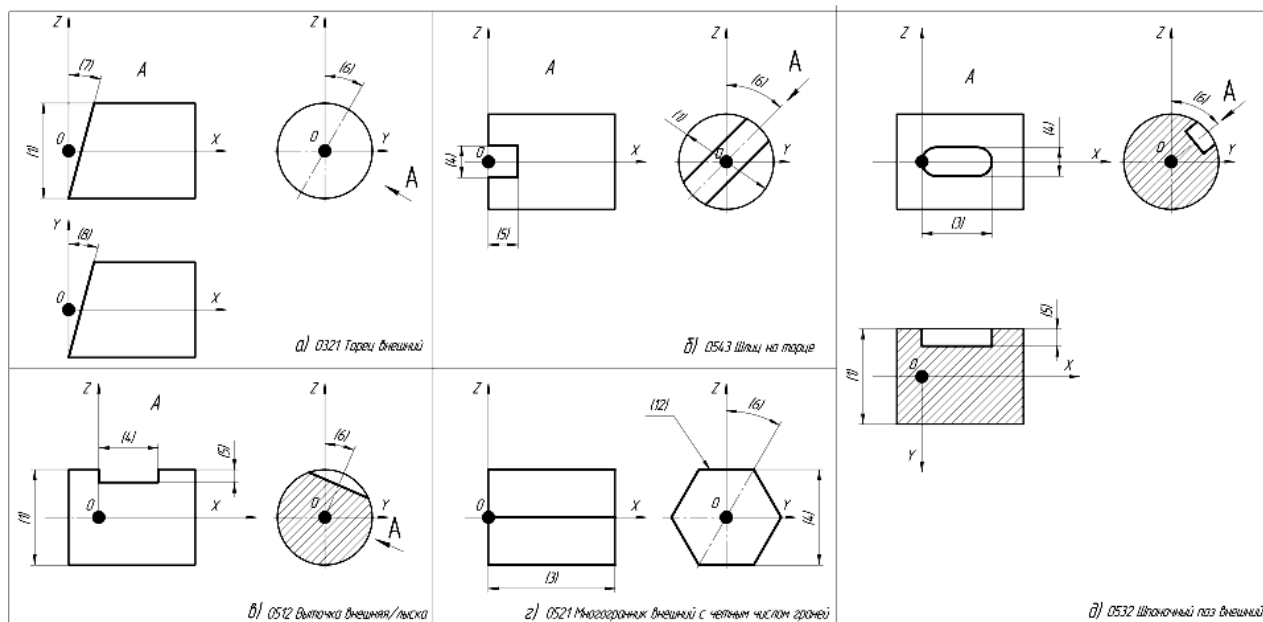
Элементарные поверхности для оборудования фрезерной группы
